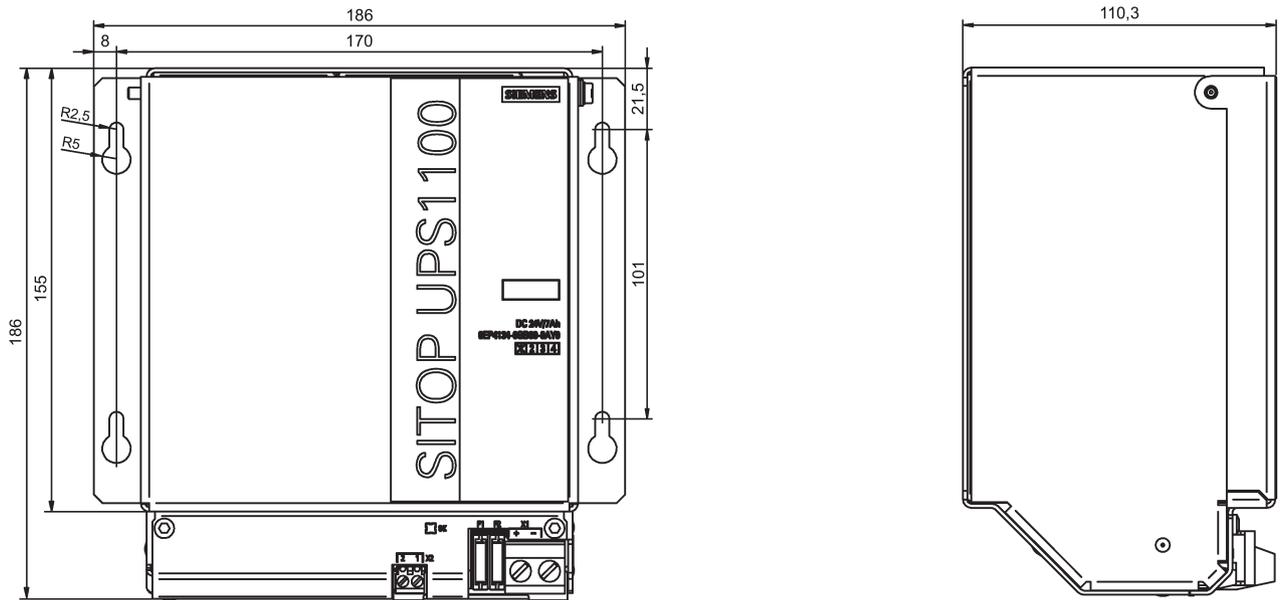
Maßzeichnung 6EP4134-0GB00-0AY0
